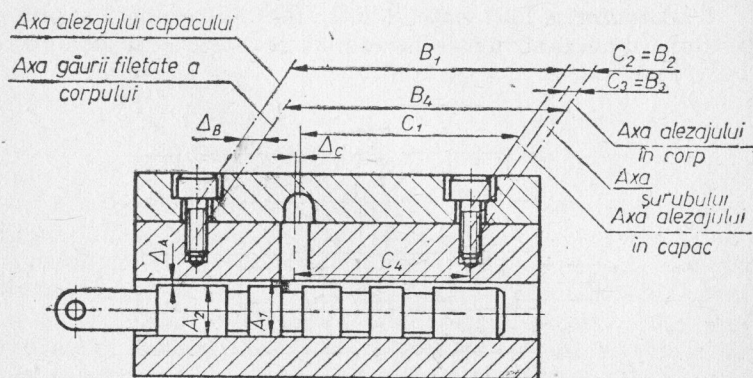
Lanțul de dimensiuni pentru sertarul din fig. 9.21.
